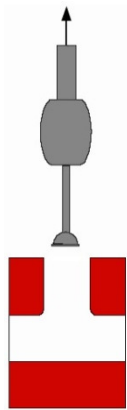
Das Werkzeug aus dem Werkstück zurückziehen.
